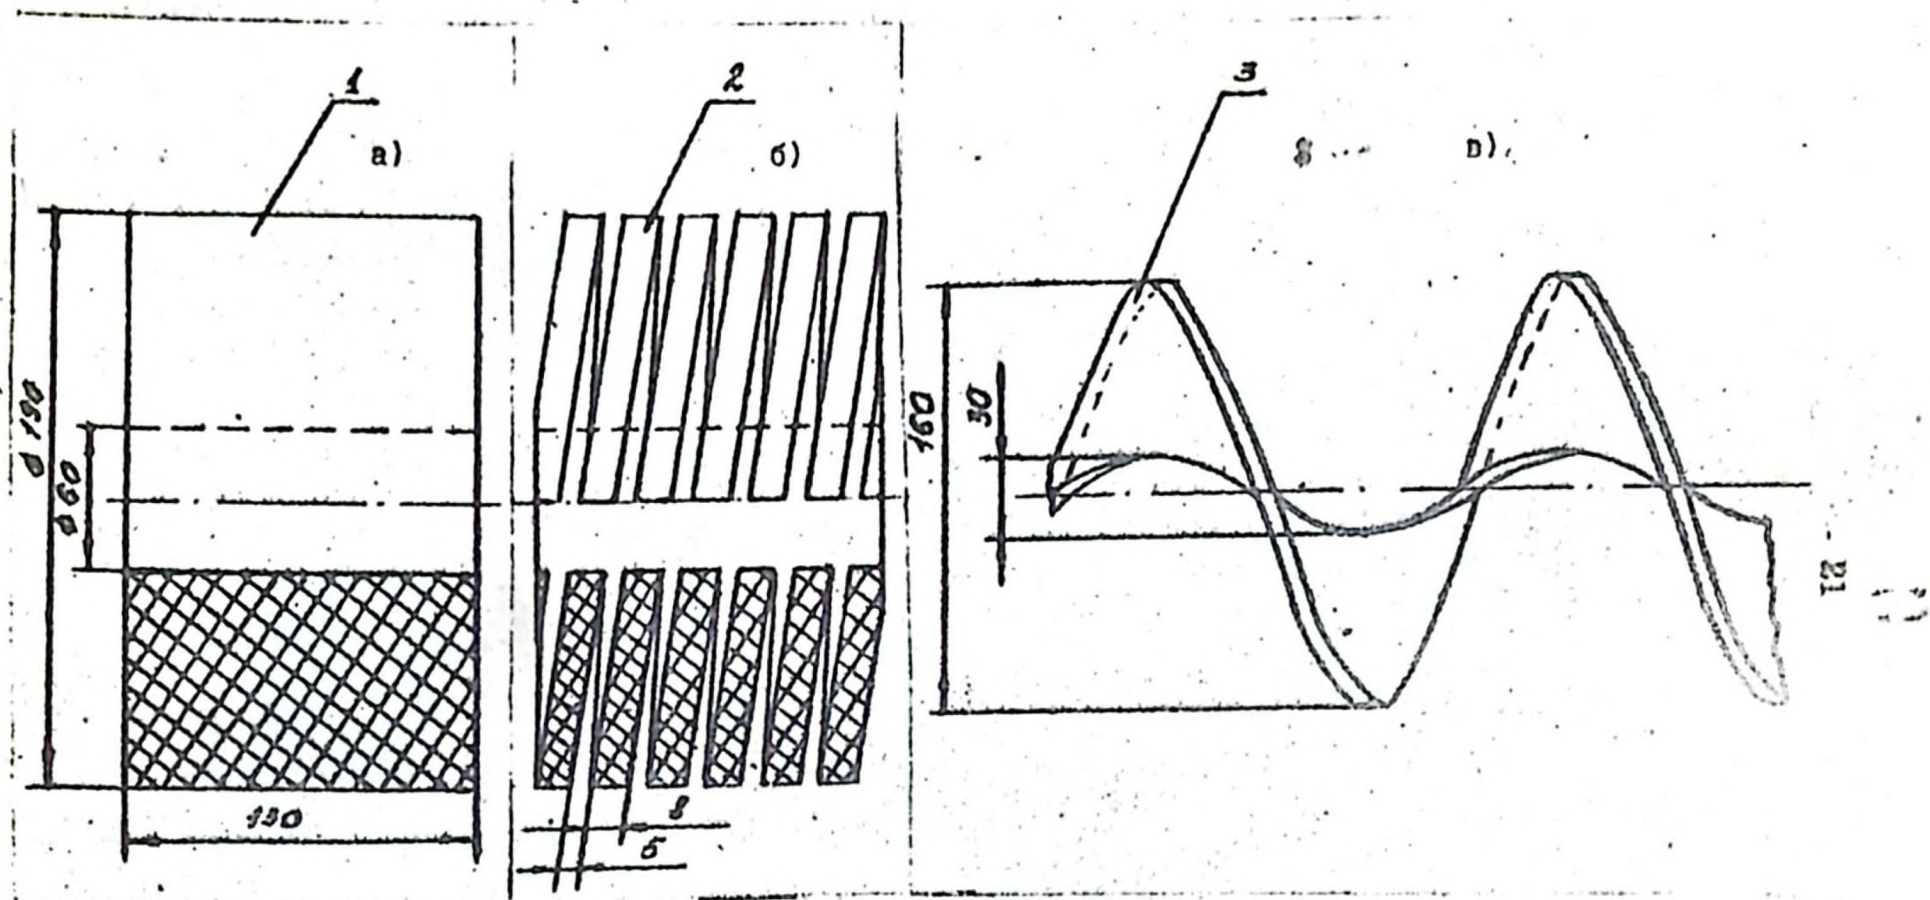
Изготовление полиэтиленового ящика шнека
